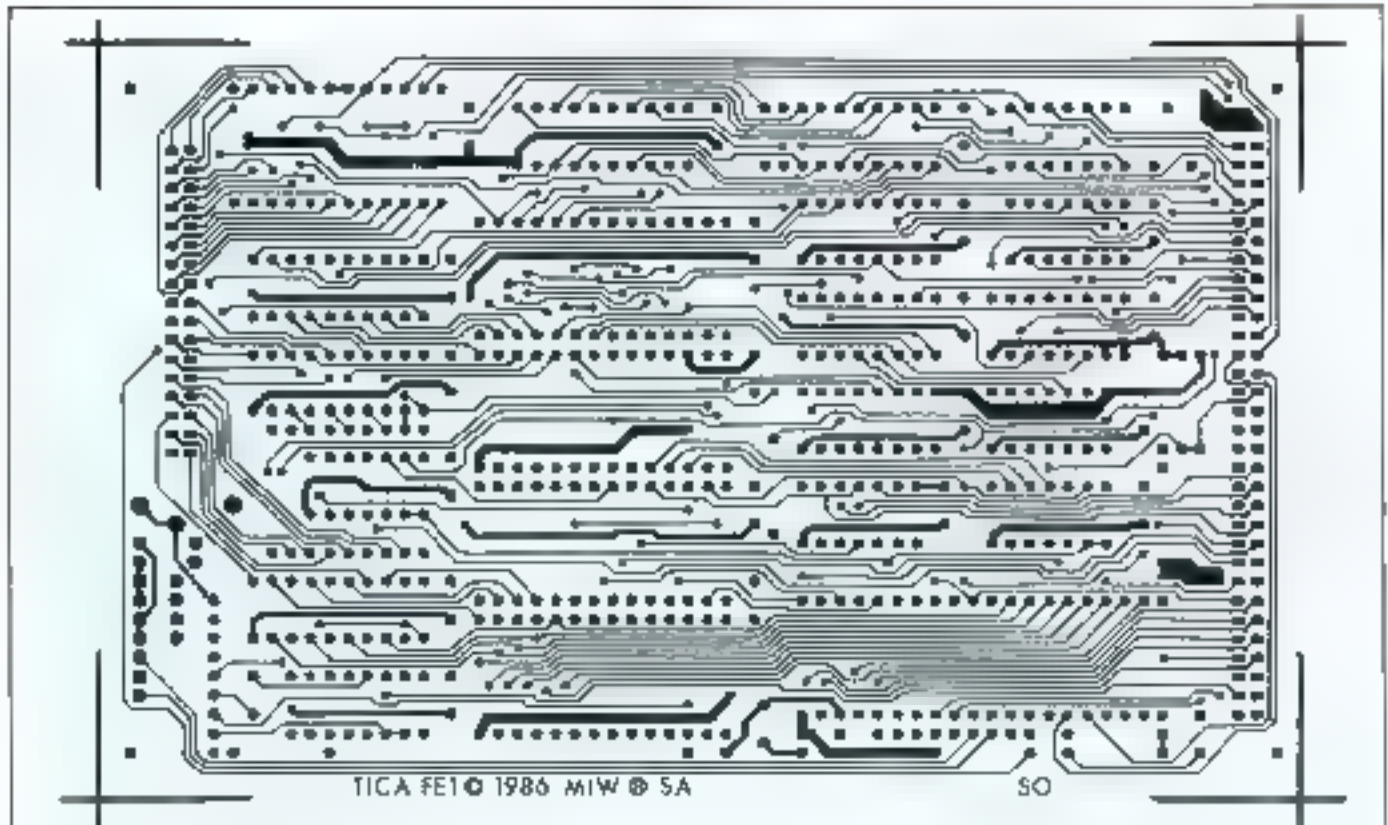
Circuit imprimé, 1400M soudures
